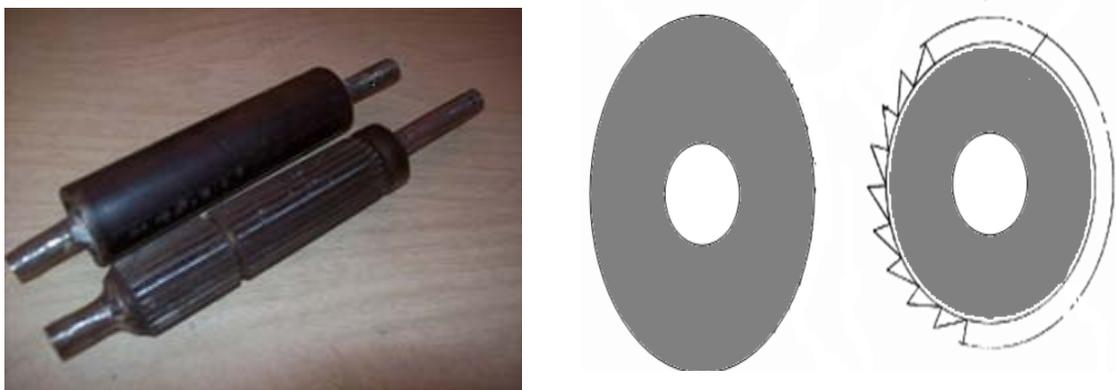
Rodillos (liso y dentado) y formas de corte por compresión.
